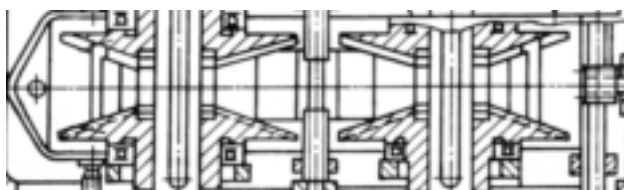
Схема зацепления дисков и пластинчатой цепи
